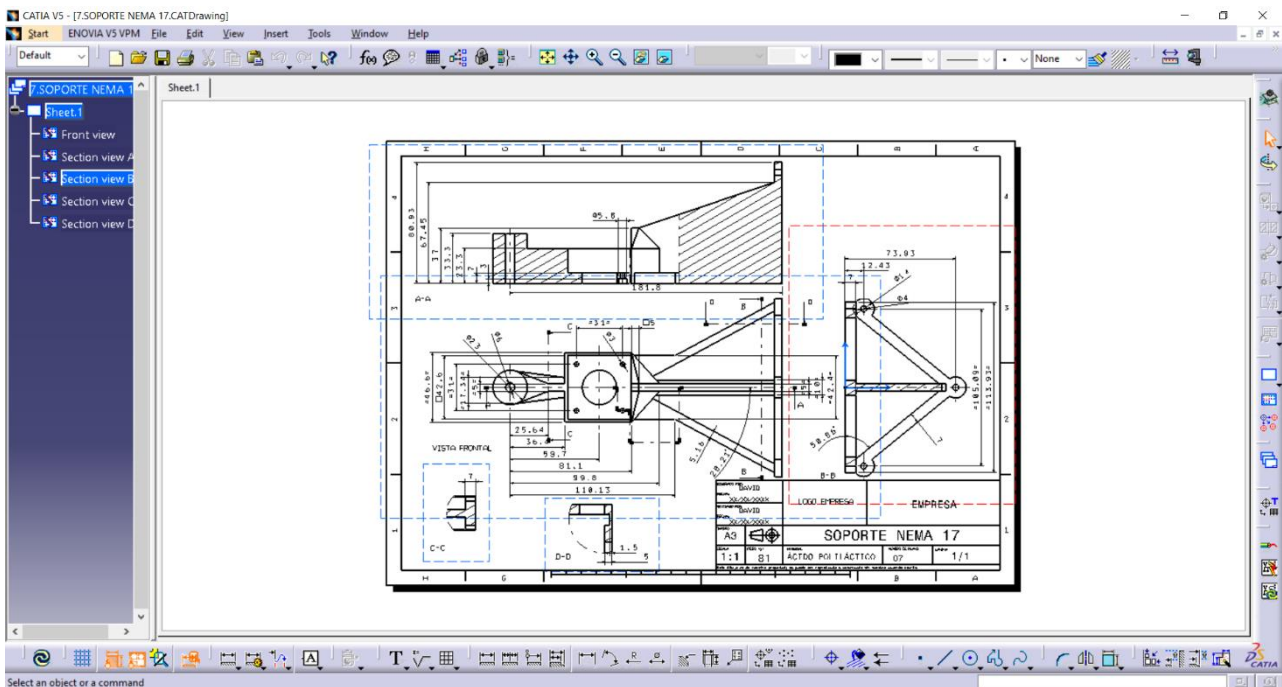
Plano de componente estructural diseñado en Módulo Drafting
